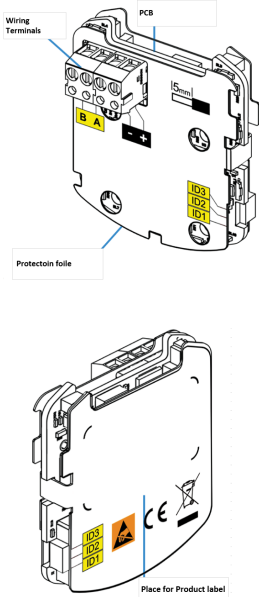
Grundplatten-Baugruppe (Frontansicht) Abb. 2: In die Grundplatte integrierte Elektronik (Rückansicht)
